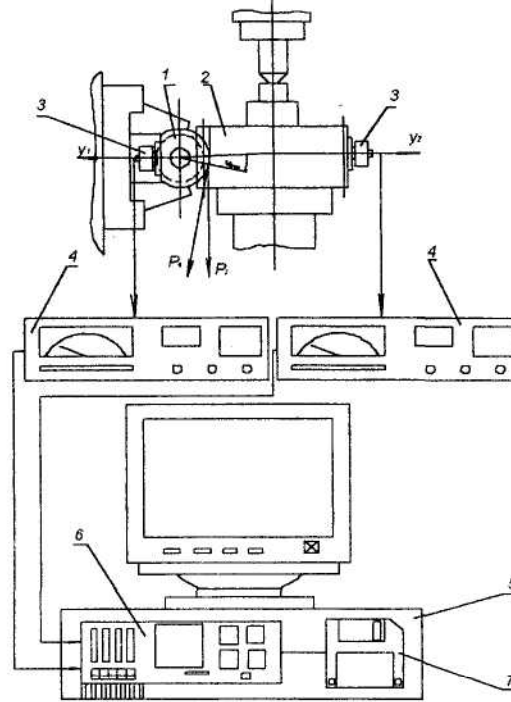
Схема вимірювання коливань у робочій зоні зубофрезерного верстата:
